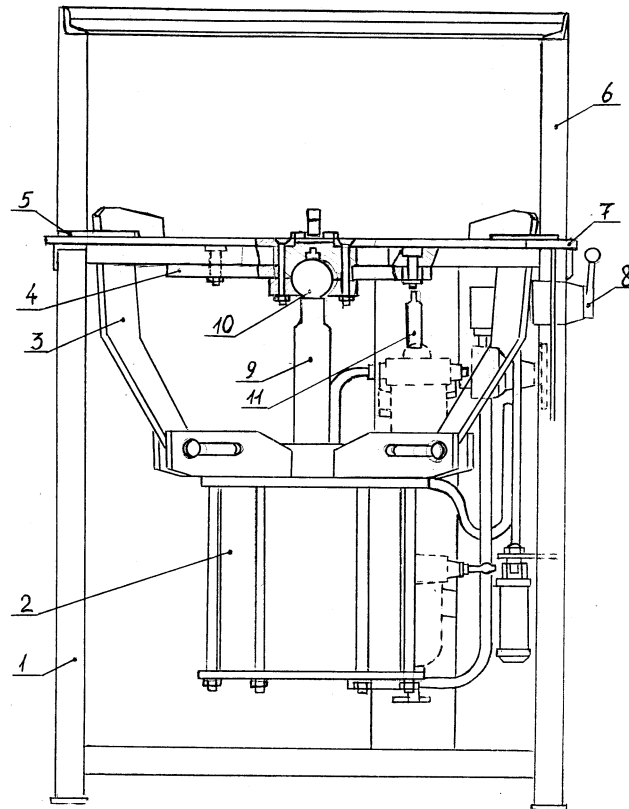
Стенд для розбирання муфт зчеплення: 1 – основа; 2 – пневмоциліндр; 4 – диск; 3 – притискач; 6 – стійка; 5 – повзун; 8 – пневморозподільник; 7 – плита; 10 – кульовий шарнір; 9 – шток; 11 – рукоятка фіксатора.
